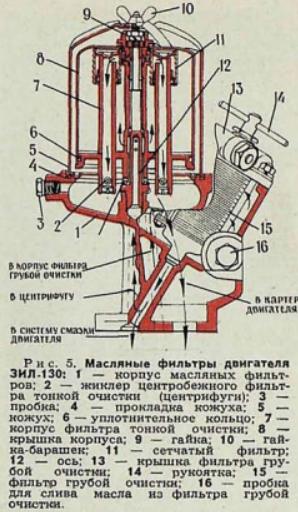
Масляные фильтры двигателя ЗИЛ-130: 1 — корпус масляных фильтров; 2 — юнкер центробежного фильтра; 3 — промывка тонкой очистки (центрифуга); 4 — кран; 5 — мокрый; 6 — универсальный фильтр конуса; 7 — крышка корпуса; 9 — гайка; 10 — гайка; 11 — сепаратор; 12 — ось; 13 — сепаратор фильтра грубой очистки; 14 — промывка фильтра грубой очистки; 15 — фильтр грубой очистки; 16 — пробка для слива масла из фильтра грубой очистки.
